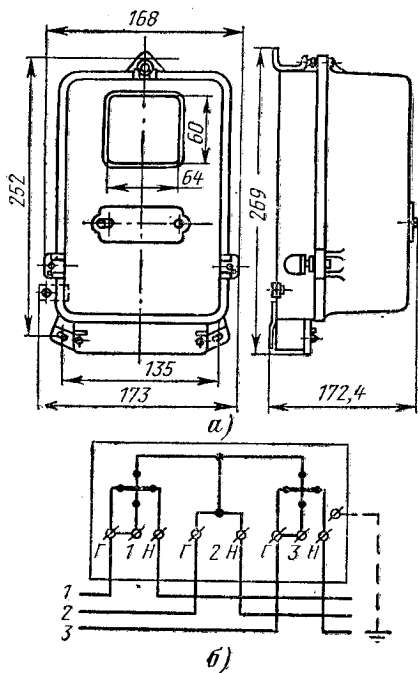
Габаритный чертеж и схема включения счетчиков типа ИТ, САЗ, САЗУ, СРЗ, СРЗУ, СР4, СР4У и ИТР.
